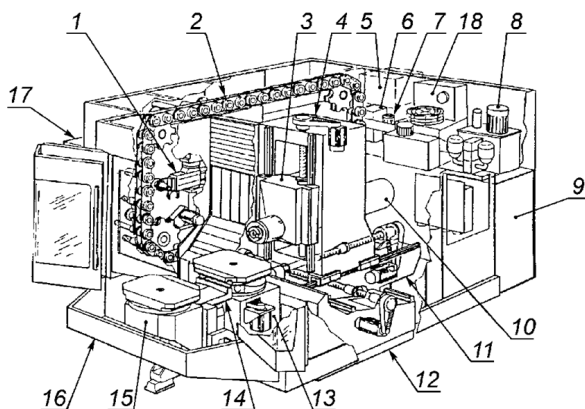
Обрабатывающий центр с горизонтальным шпинделем и маятниковым устройством смены инструмента: 1 – устройство автоматической смены инструмента; 2 – инструментальный магазин; 3 – передняя бабка с горизонтальным рабочим шпинделем; 4 – станина с приводом подачи, ось Y; 5 – брызгоуловитель; 6 – централизованная смазка; 7 – пневматический узел; 8 – гидравлический узел; 9 – шкаф распределительного устройства; 10 – главный привод; 11 – крестовые салазки с приводом подачи, ось Z; 12 – станина с приводом подачи, ось X; 13 – круглый стол с ЧП; 14 – устройство смены паллет; 15 – место монтажа; 16 – закрытая кабина; 17 – устройство для сбора и удаления смазочно-охлаждающей жидкости и стружки; 18 – агрегат для охлаждения моторного шпинделя [8]
